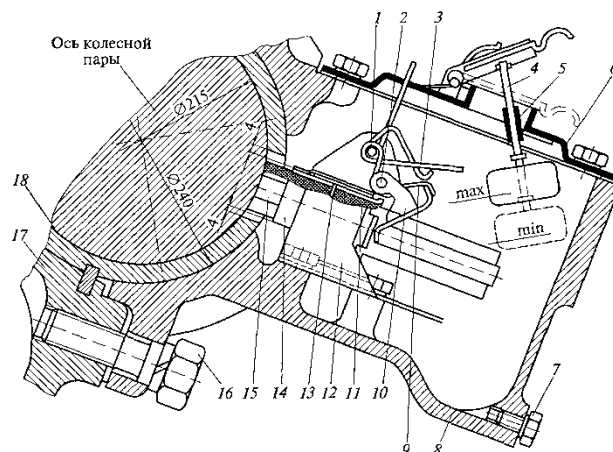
Моторно-осевой подшипник и система смазки электродвигателей ЭД118Б и ЭД125Б.
